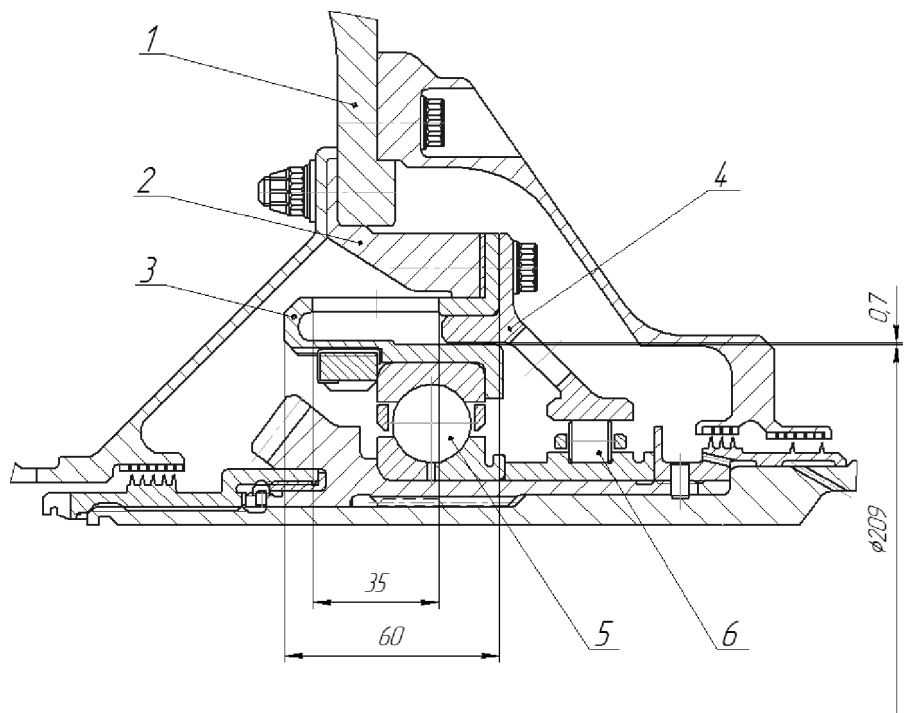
Опора РУП КВД двигателя CFM56-7
